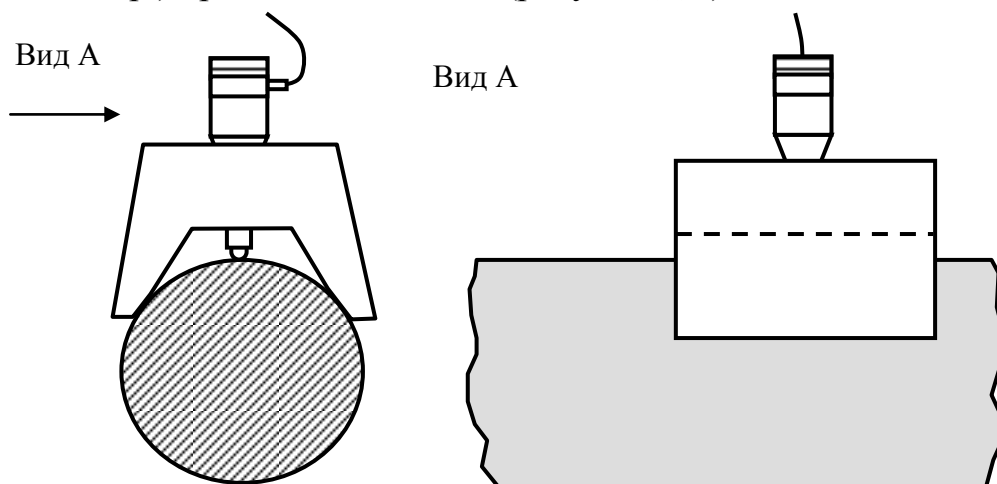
Насадки для контроля деталей с круглым сечением
